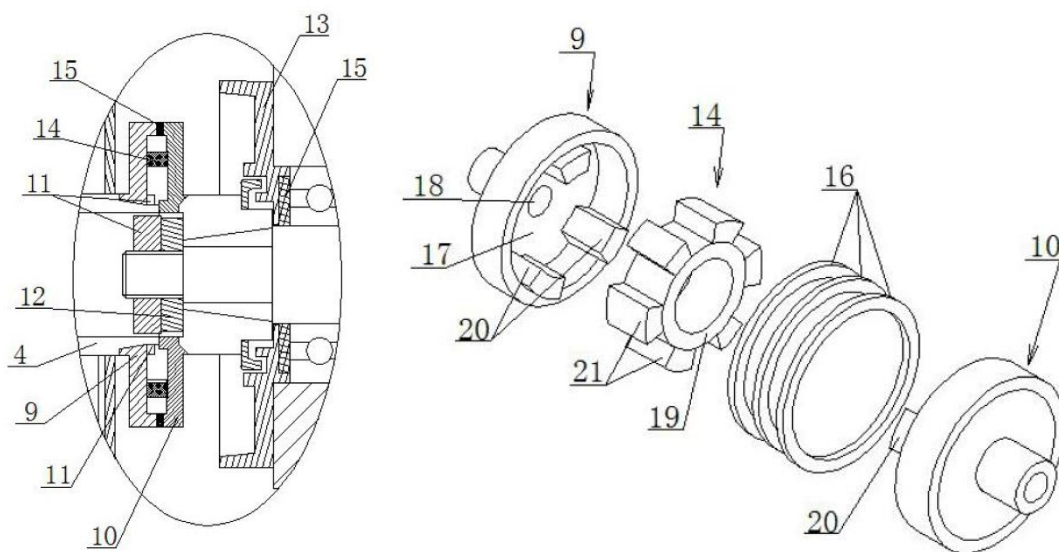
9 – Почвообрабатывающая фрезы с устройством защиты от поломок:
